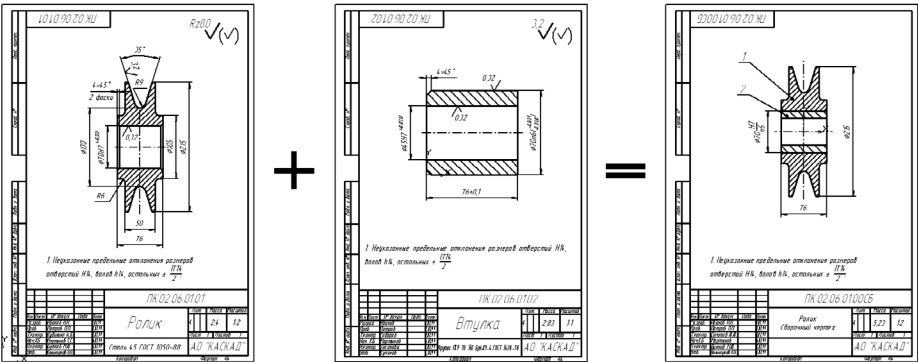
Создание сборочного чертежа «снизу вверх»
